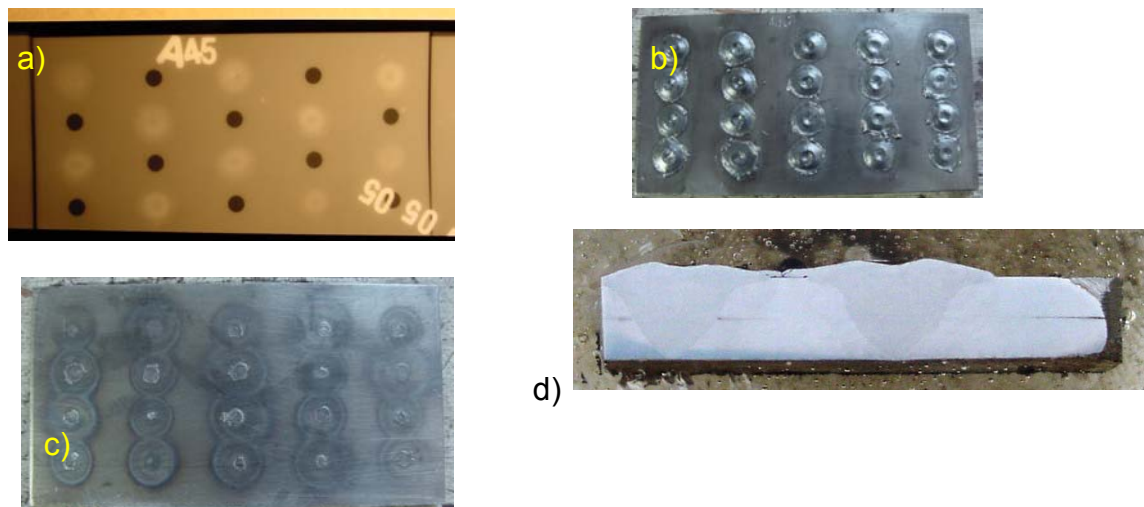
Soldas com o procedimento MIG/MAG convencional desenvolvido: a) raios-X, b) face das soldas, c) fundo das soldas, d) seção transversal.
